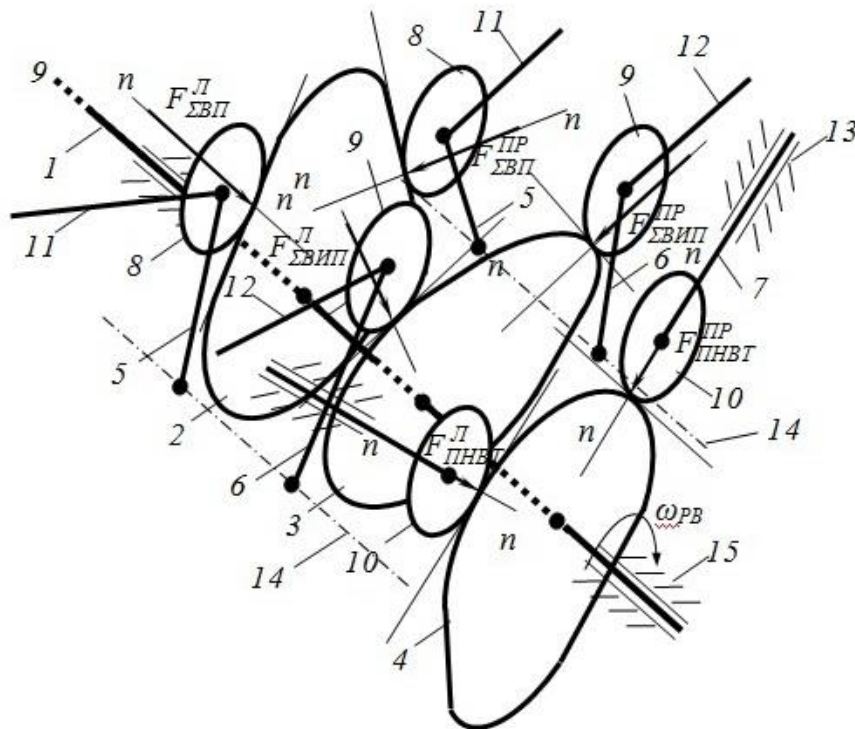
Формування навантажень, діючих на елементи конструкції РВ енергетичної установки тепловоза з дизелем Д49: 1 – розподільний вал; 2 – впускний кулачок; 3 – випускний кулачок; 4 – паливний кулачок; 5 – коромислові штовхачі привода ВПК; 6 – коромислові штовхачі привода ВИПК; 7 – штовхач ПНВТ; 8...10 – ролики штовхачів; 11 – штанги привода ВПК; 12 – штанги привода ВИПК; 13 – напрямні штовхачів ПНВТ; 14 – осі коромислових штовхачів; 15 – опора РВ
